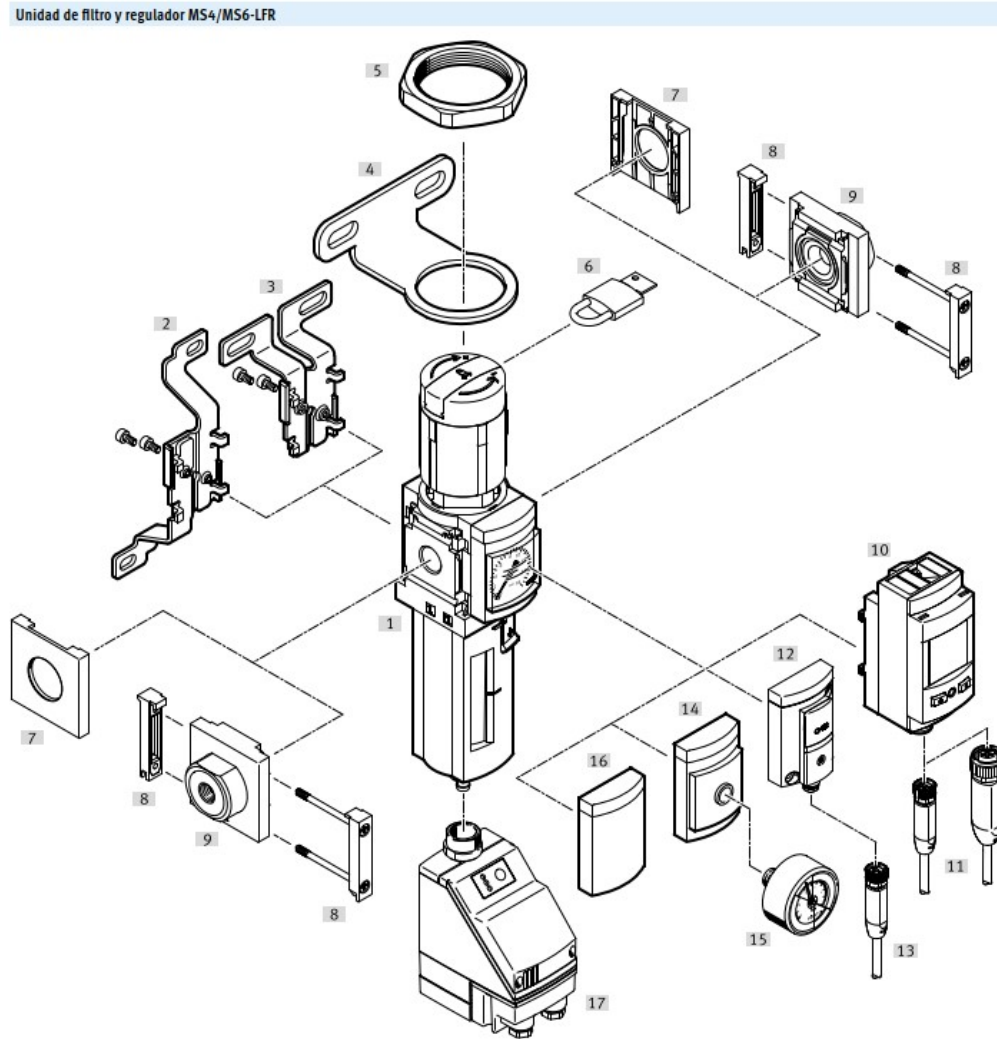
Conjunto de accesorios del filtro-regulador.
